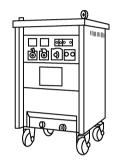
ZX5-400 型晶 闸管整流弧焊机外形
